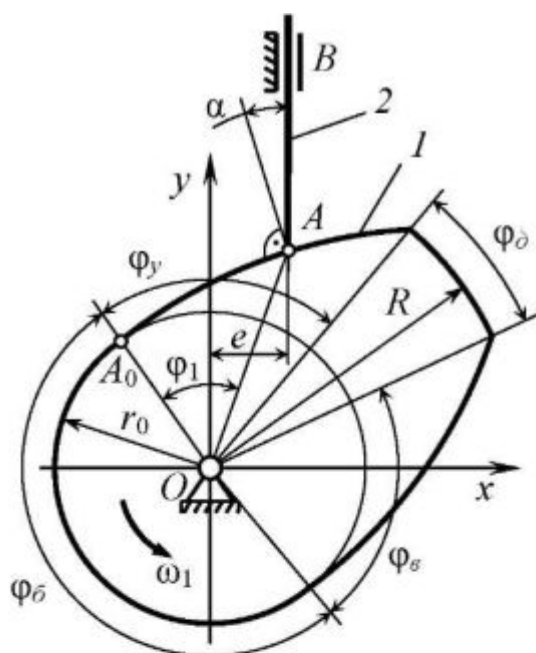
Основные параметры кулачковых механизмов с поступательно движущимся толкателем
